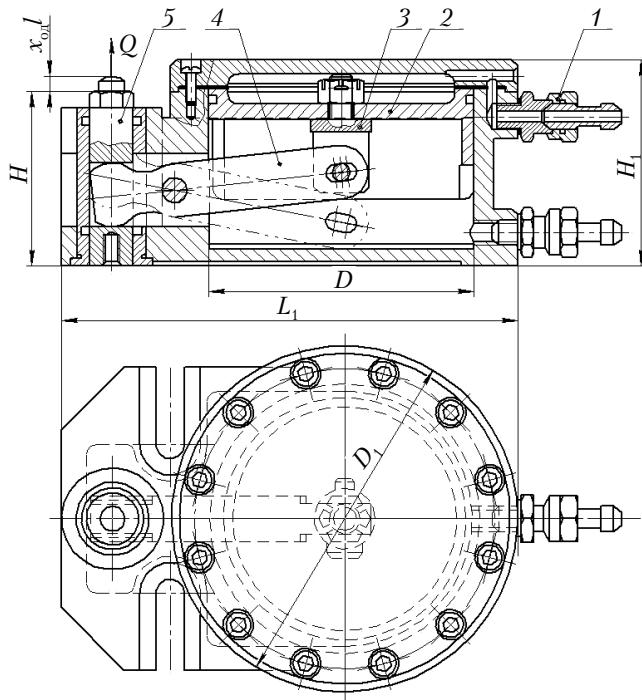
Агрегатируемый универсальный пневмоцилиндр с рычажным усилителем
